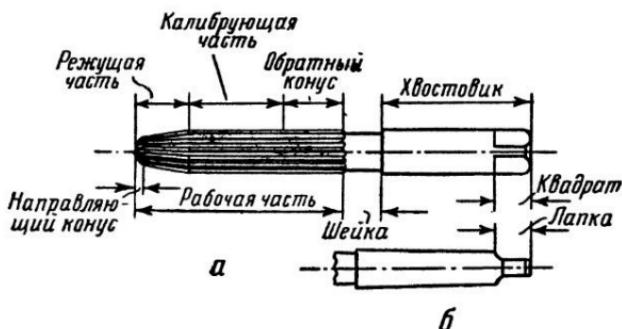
Цилиндрическая развертка и ее составные части: *а* — общий вид развертки; *б* — конический хвостовик.
